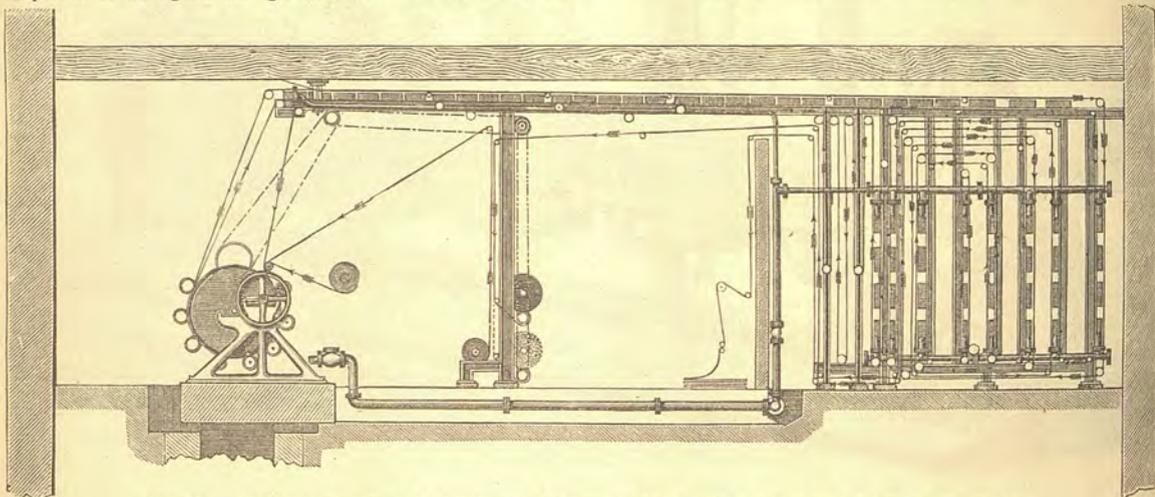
Macchina a stampare a 8 colori, con disposizione per l'asciugamento del tessuto stampato.
